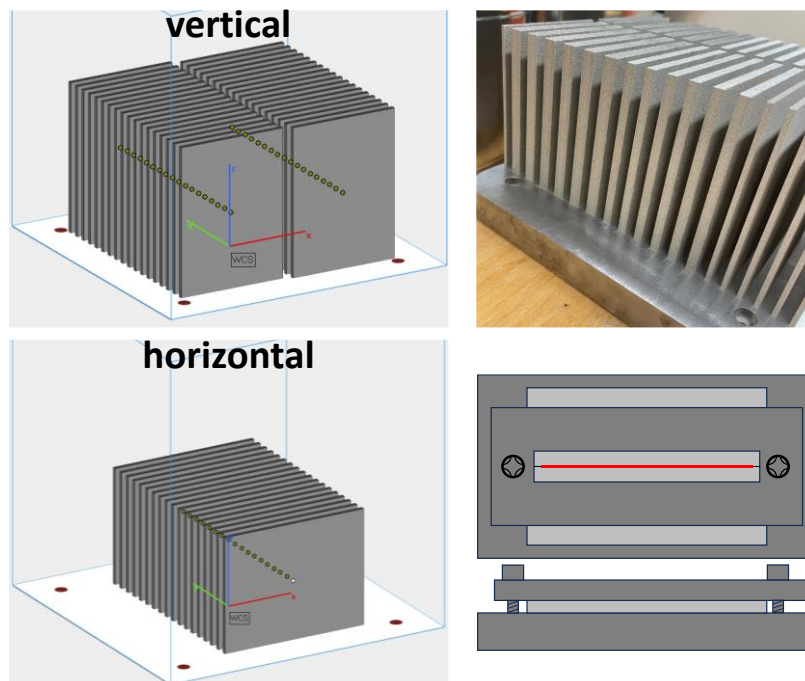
Ausrichtung der Bauteile sowie für das Schweißen verwendete Spannvorrichtung.
